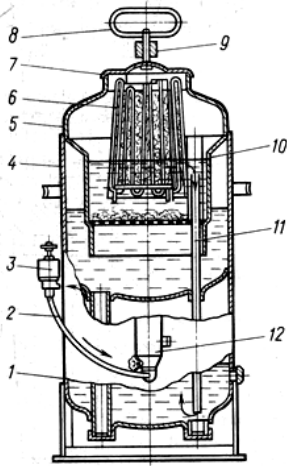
Генератор АСМ-1,25-3: 1 – нижняя часть корпуса, которая называется промывателем; 2 – шланг; 3 – клапан; 4 – корпус; 5 – верхняя часть (корпус) шахты; 6 – корзина с карбидом кальция; 7 – крышка; 8 – винт; 9 – запор; 10 – шахта; 11 – трубка, по которой ацетилен опускается в промыватель; 12 – водяной затвор; 13 – манометр
